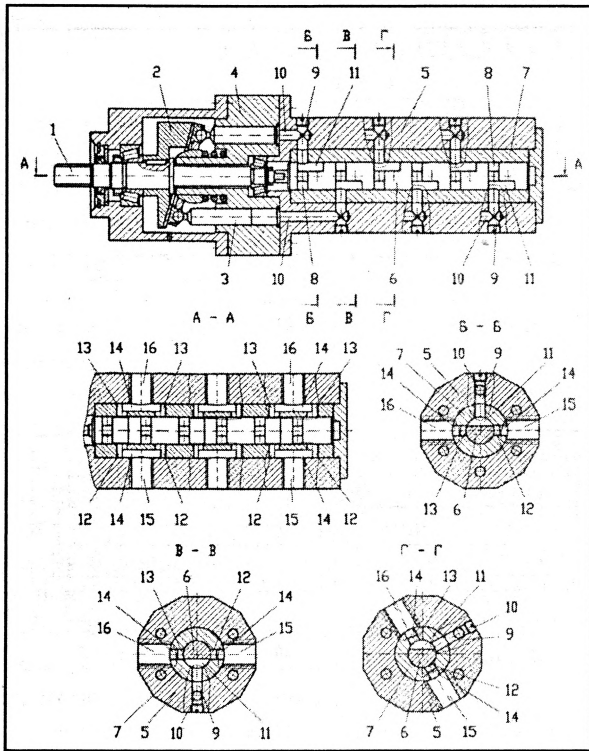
Многопоточная аксиально-поршневая гидромашина с неподвижным блоком цилиндров: 1 — ведущий вал; 2 — наклонная шайба; 3 — поршень; 4 — блок цилиндров; 5 — корпус гидрораспределителя; 6 — вал гидрораспределителя; 7 — подшипник скольжения; 8 — кольцевая канавка; 9, 10, 15, 16 — каналы корпуса гидрораспределителя; 11 — сегментный паз; 12, 13 — каналы подшипника скольжения; 14 — пазы подшипника скольжения
